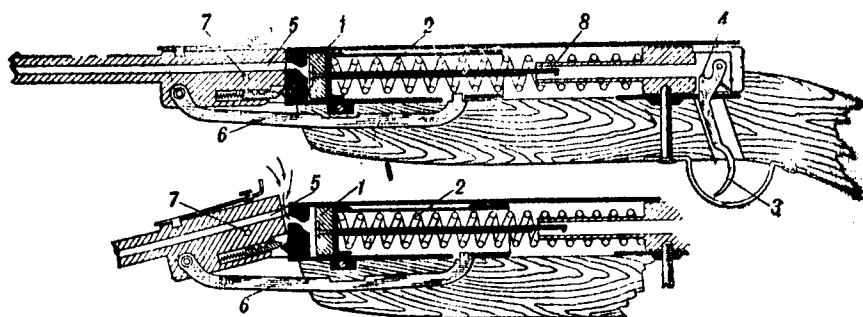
Схема устройства и действия пневматической винтовки. Вверху — положение после выстрела; внизу — момент заряжания. 1 — поршень, 2 — пружина поршня; 3 — спусковой крючок; 4 — шептало; 5 — место, куда вкладывается пуля; 6 — рычаг; 7 — ось вращения ствола винтовки; 8 — боевой взвод.
